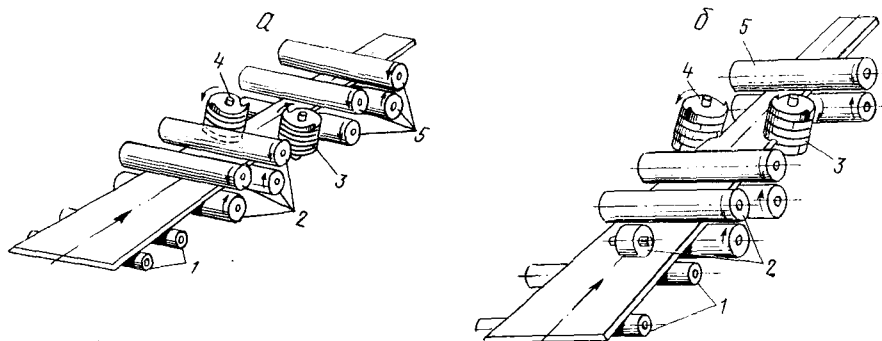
Принципиальная схема станка для фрезерования кромок досок: а — с попутной подачей; б — с симметрично раздвигающимися наклонными головками; 1 — загрузочный стол; 2 — подающие вальцы; 3, 4 — фрезерные головки; 5 — задние вальцы
